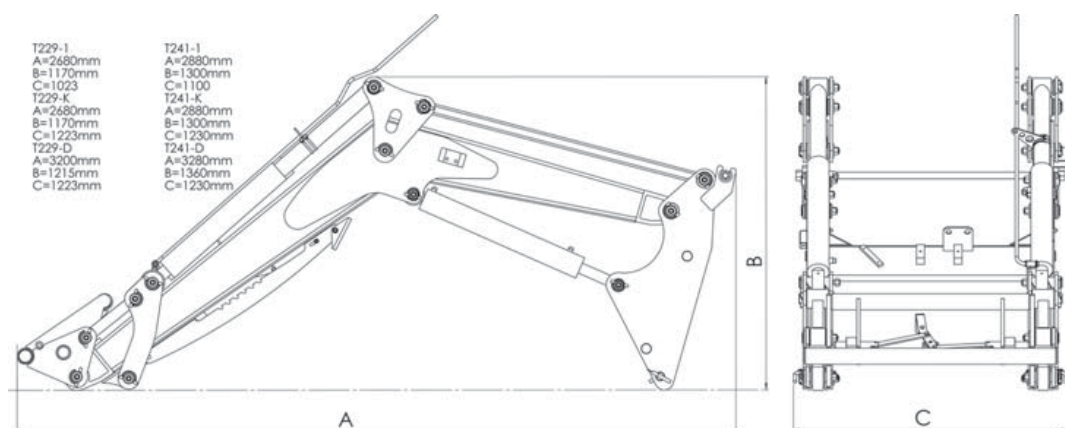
Размеры погрузчика, подготовленного для транспортировки
